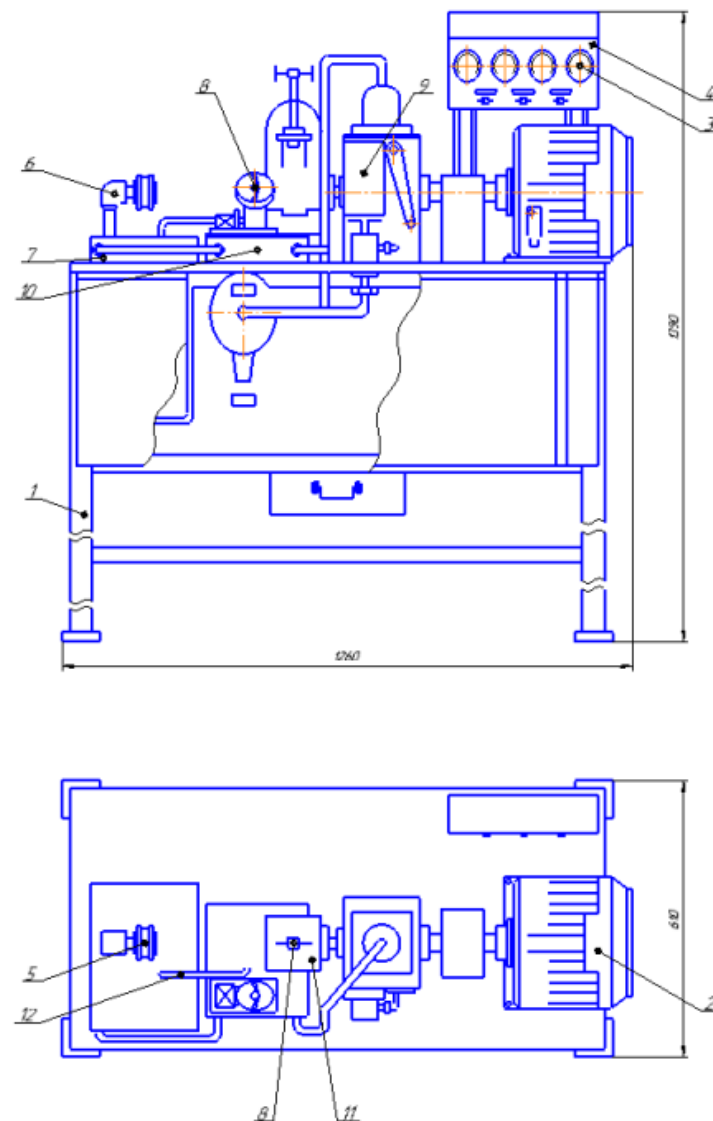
Стенд для перевірки і регулювання оливних насосів: 1 – станина; 2 – електродвигун; 3 – манометр; 4 – панель керування; 5 – штуцерний пристрій; 6 – впускний трубовід; 7 – бак; 8 – кран; 9 – двоступеневий редуктор; 10 – плита; 11 – витратомір; 12 – шланг.
